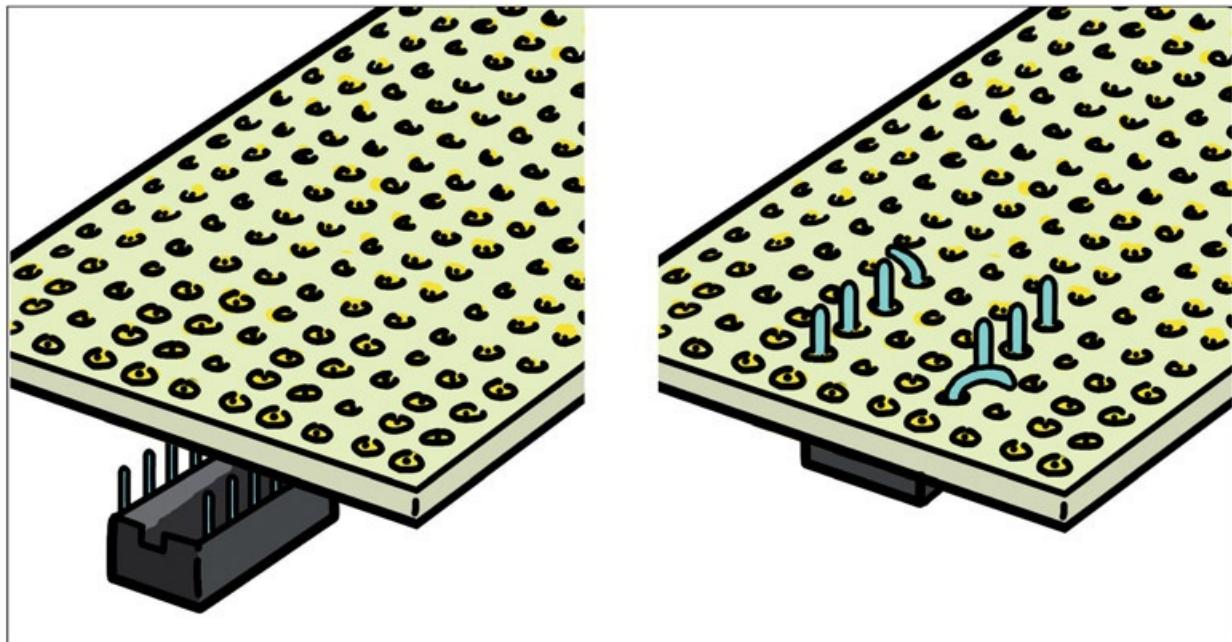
Soldadura de un zócalo para un chip sobre una placa de prototipo.
